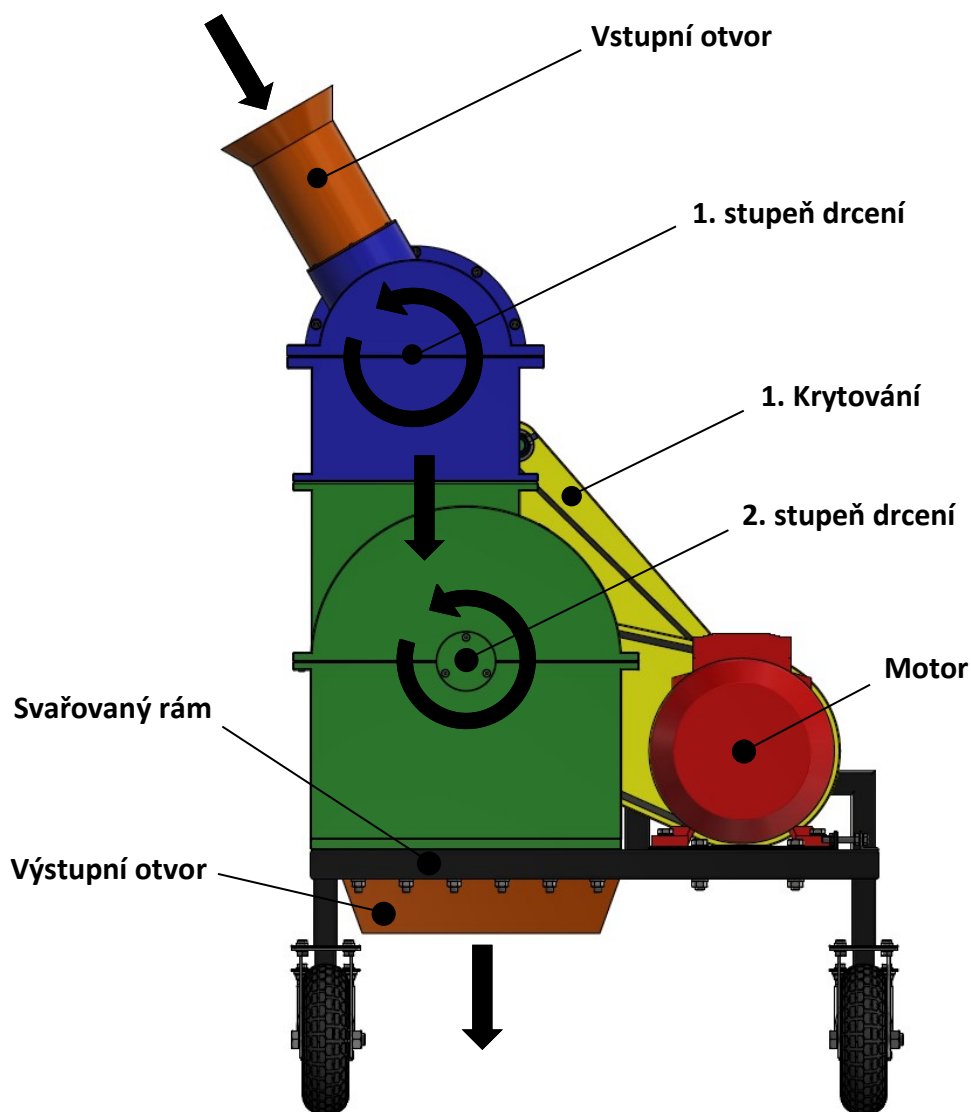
Zahradní drtič PROMA MZD-13/102 s vícestupňovou desintegrací [18]
